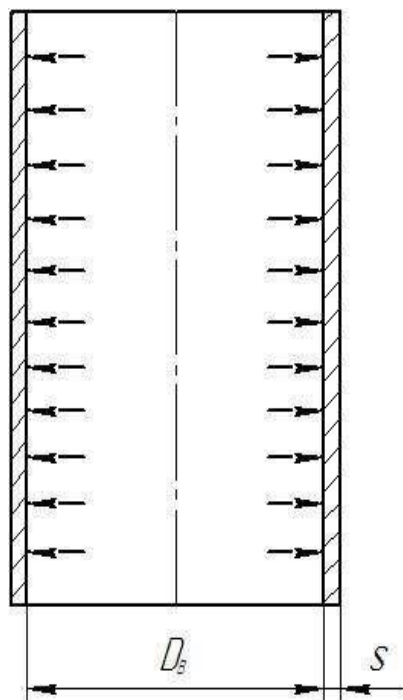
Розрахункова схема обичайки корпусу, навантаженого внутрішнім тиском
